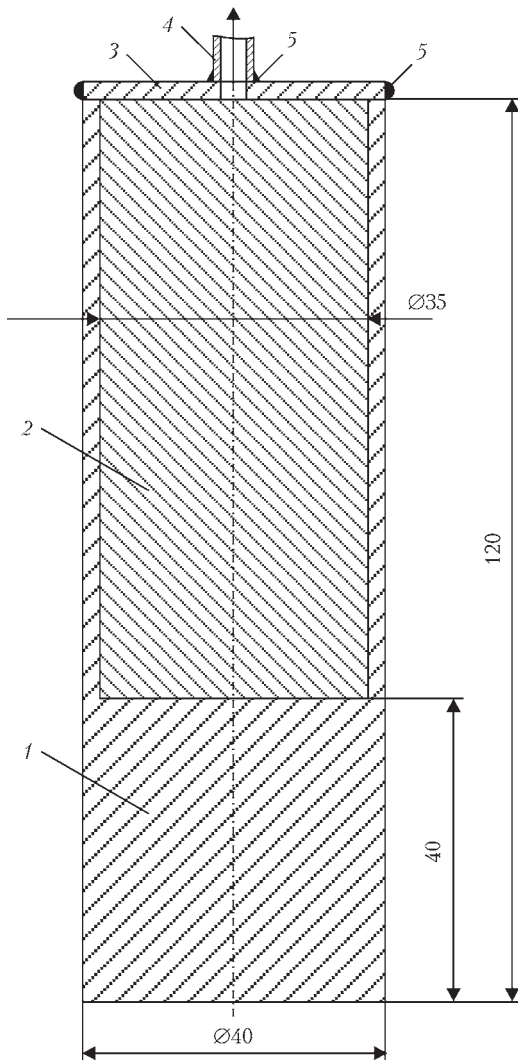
Эскиз опытной заготовки для пайки: 1 — полый цилиндр; 2 — расплавляемый компонент (медь); 3 — крышка; 4 — патрубок для вакуумирования; 5 — герметизирующие сварные швы
